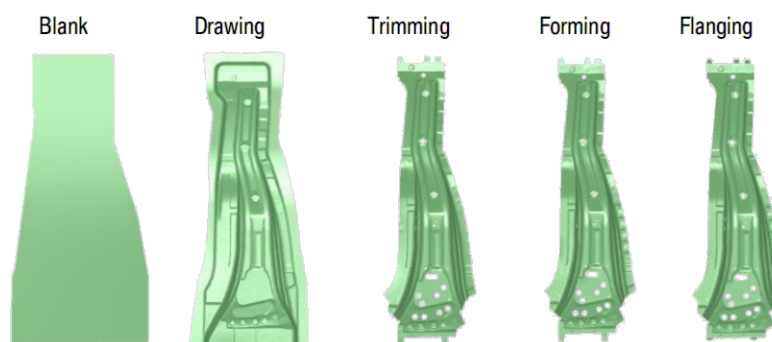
Вытяжка, обрезка, формовка и догибка листового изделия. Источник: [51]
